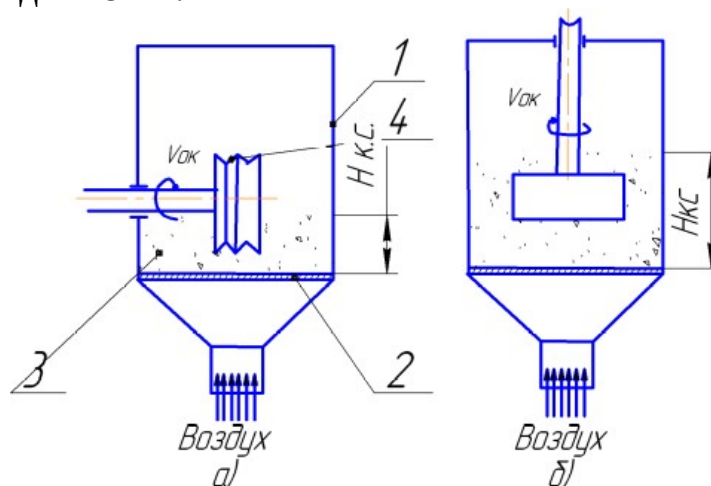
Схема процесса турбоабразивной обработки: а – с горизонтальной осью вращения заготовки; б – с вертикальной: 1 – рабочая камера; 2 – воздухораспределительная решетка; 3 – абразивное зерно; 4 – заготовка
